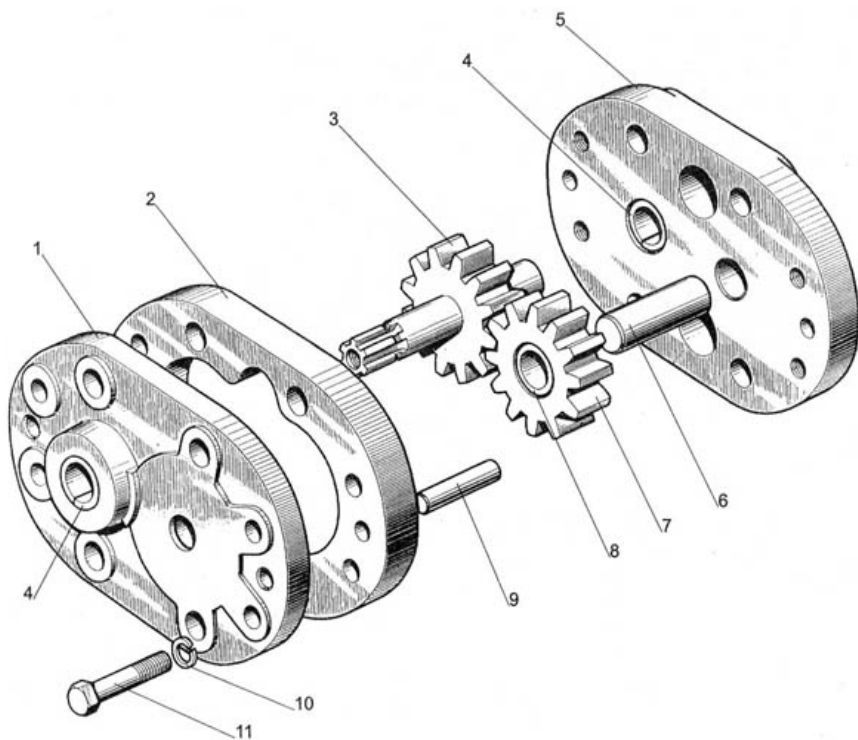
Конструкция шестеренного насоса с внешним зацеплением шестерен
